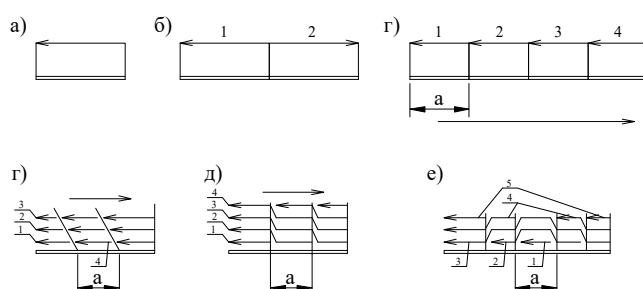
Схема выполнения сварных швов: а – напроход; б – от середины; в – обратноступенчатый; г – блоками; д – каскадами; е – горкой.
